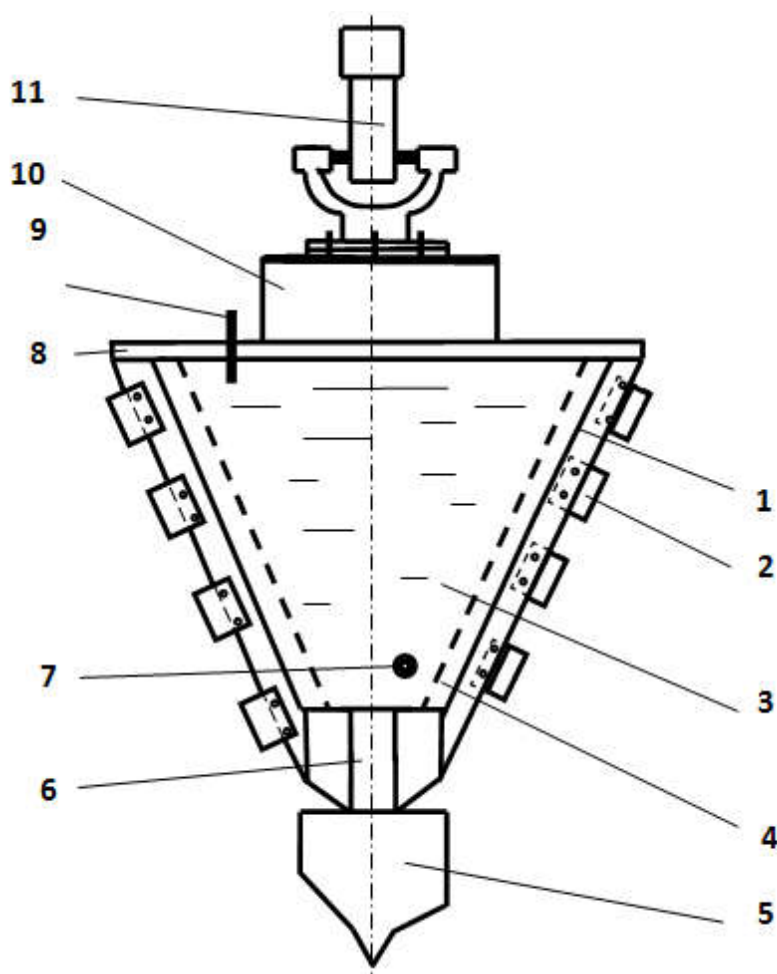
Схема конической фрезы с жидким наполнителем
